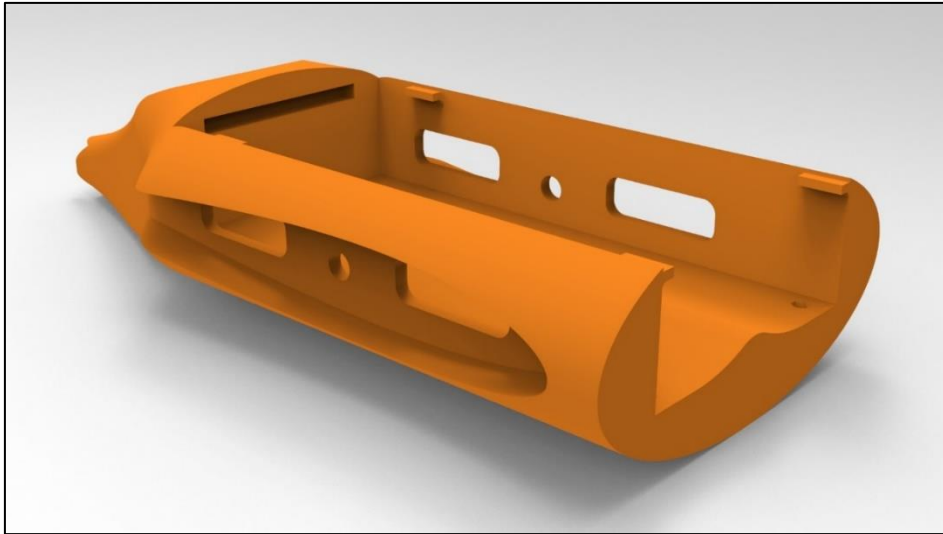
Cuerpo del fuselaje – vista isométrica frontal [Autores].
